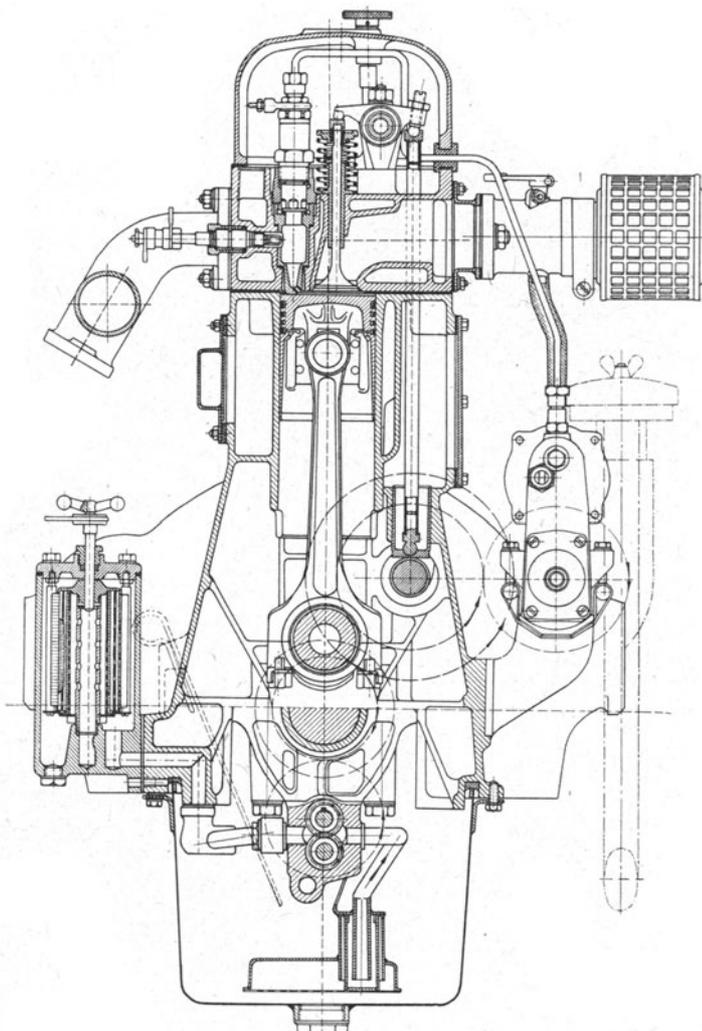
Fahrzeugdieselmotor der Klockner-Humboldt-Deutz A G (Werk Magirus).
